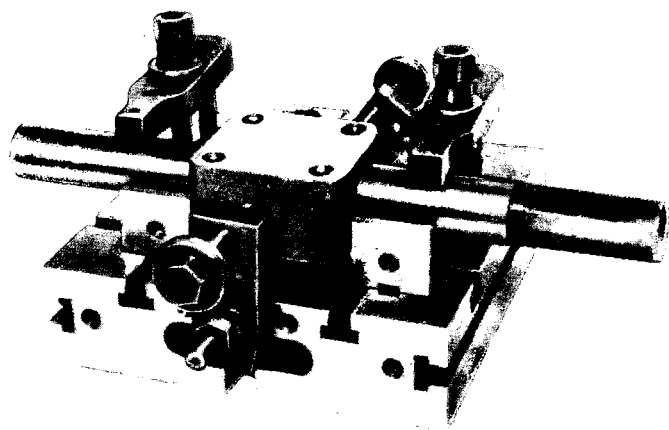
Приспособление для шлифования плоскости от базового отверстия колодки
